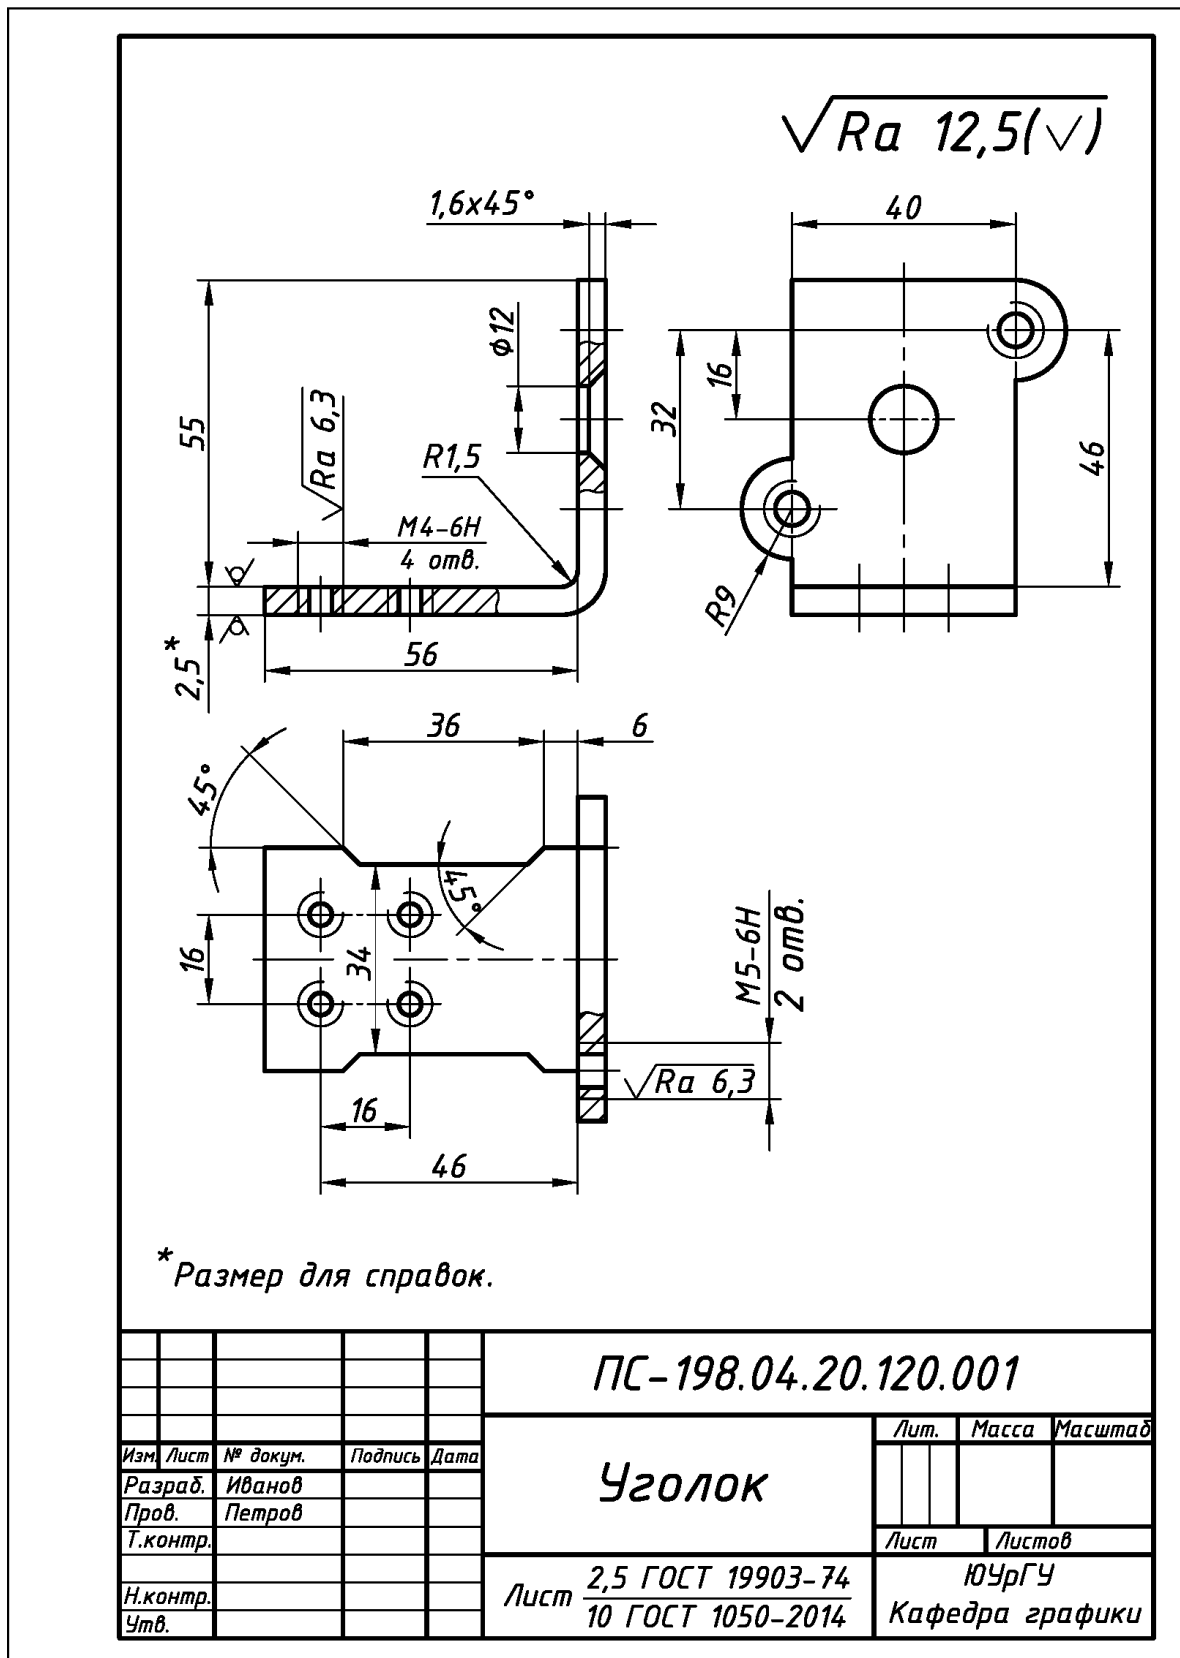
Пример выполнения и оформления эскиза детали «Уголок», изготовленной из тонколистового металла операциями «Вырубка» и «Гибка»
